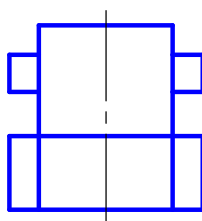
Чертеж детали, содержащий два вида: спереди и слева.
